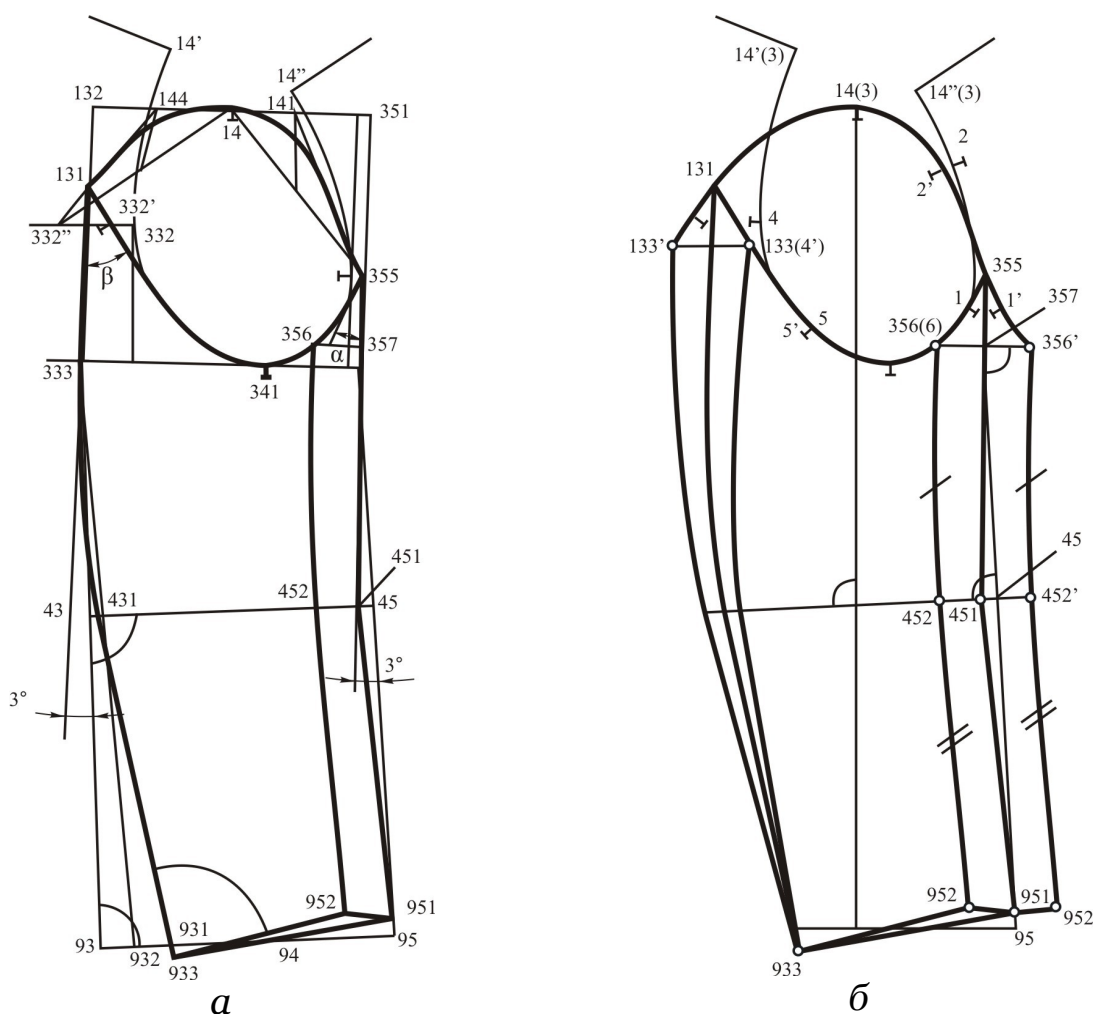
Схема разверток чертежей узла и деталей рукава
